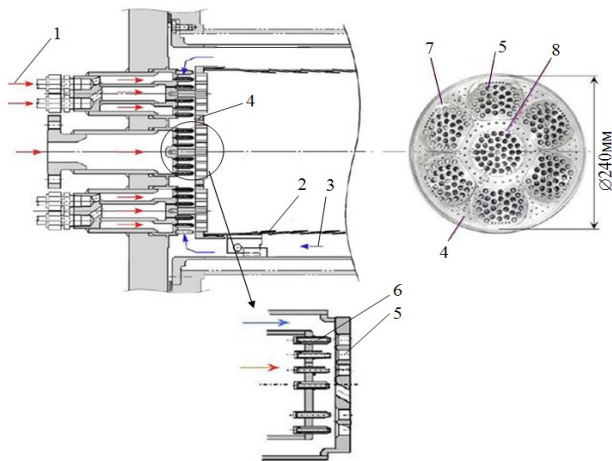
Багатопаливний паливоспалюючий пристрій фірми Hitachi:
